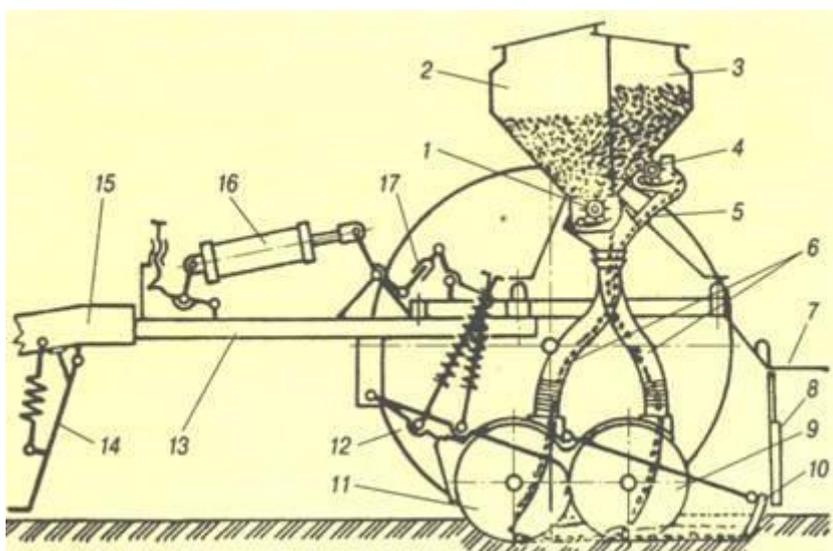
Схема робочого процесу зернотукової рядкової сівалки СЗ-3,6А:
